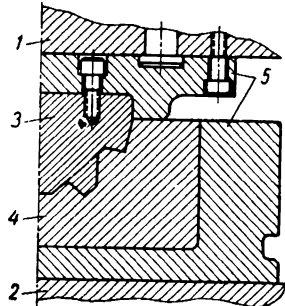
Штамповка матрицы для буровой коронки за один удар на высокоскоростном молоте фирмы «U. S. I.»: 1 — верхняя плита; 2 — нижняя плита; 3 — мастер-пуансон; 4 — штампуемая матрица; 5 — обойма
